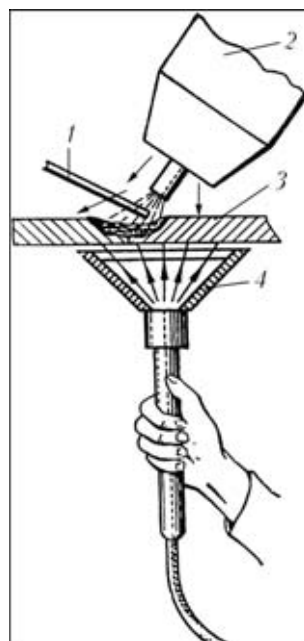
Схема защиты корня шва при выполнении ремонтной сварки: 1 — присадка; 2 — горелка; 3 — изделие; 4 — местный поддув
